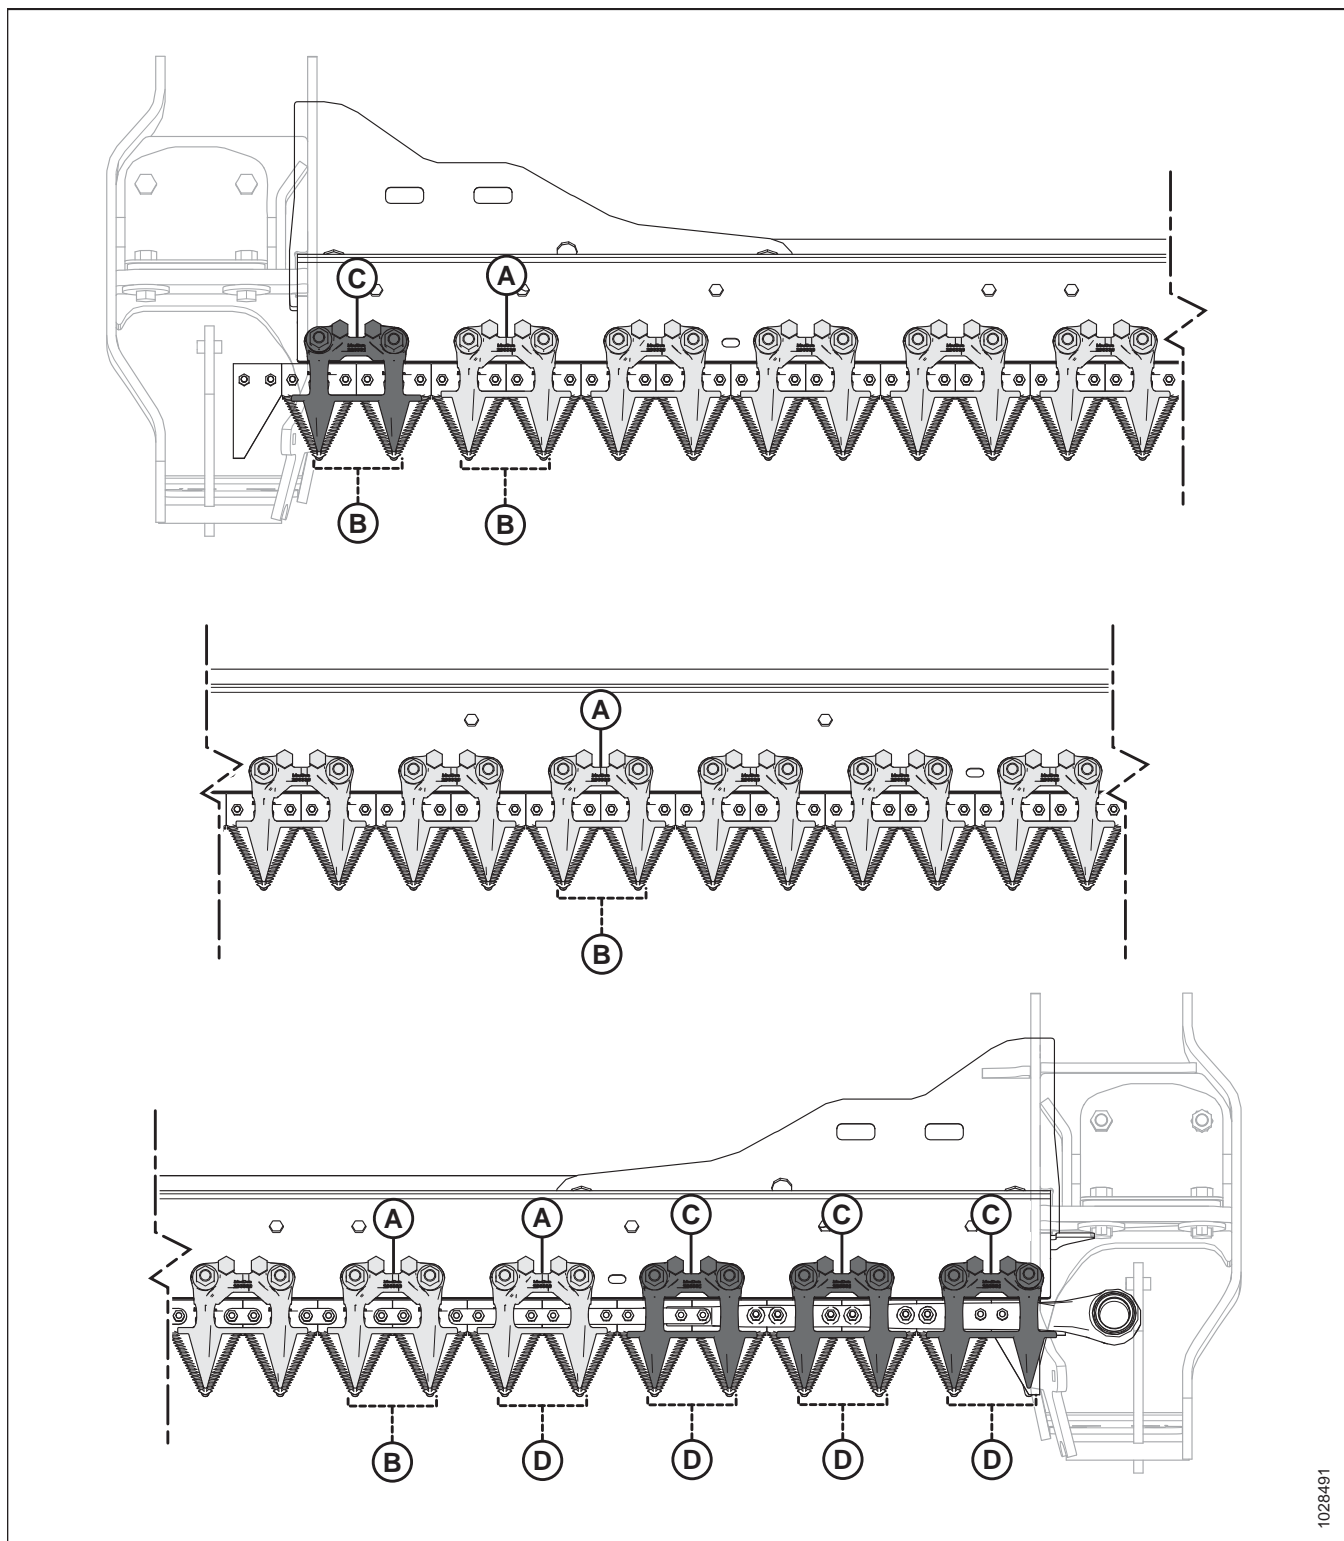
Местоположение укороченных противорезущих пальцев и прижимов — жатки с одинарными ножами
